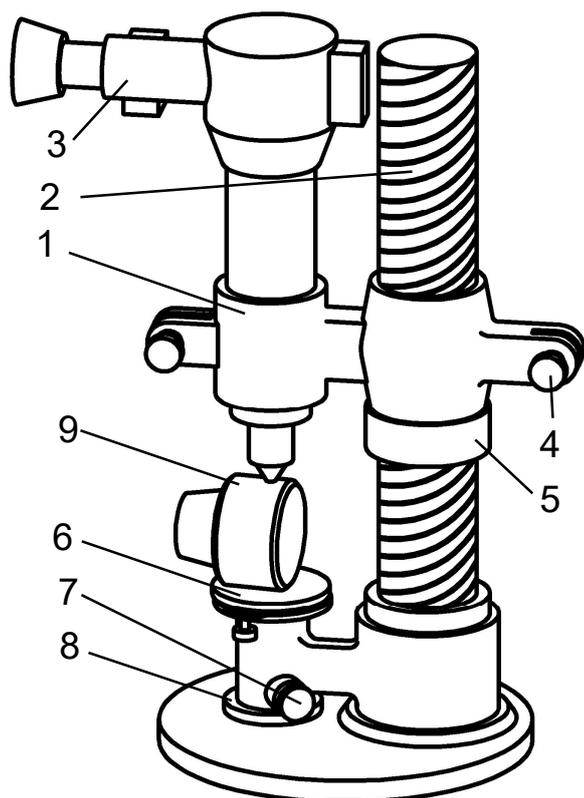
Общий вид оптиметра ОВО-1: 1 – кронштейн; 2 – стойка; 3 – трубка оптиметра; 4 – винт; 5 – резьбовое кольцо; 6 – предметный столик; 7 – винт; 8 – гайка; 9 – измеряемый образец
